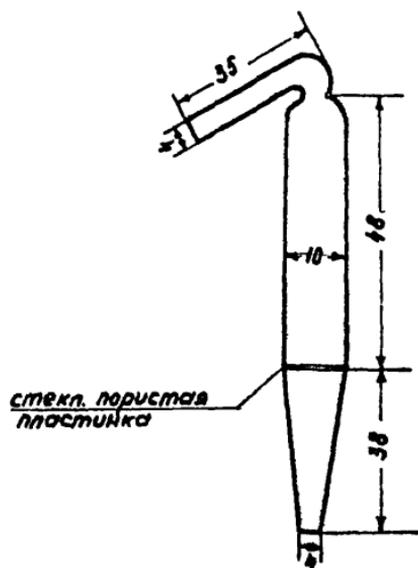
Стеклянная трубка с пористой пластинкой для отбора проб воздуха
